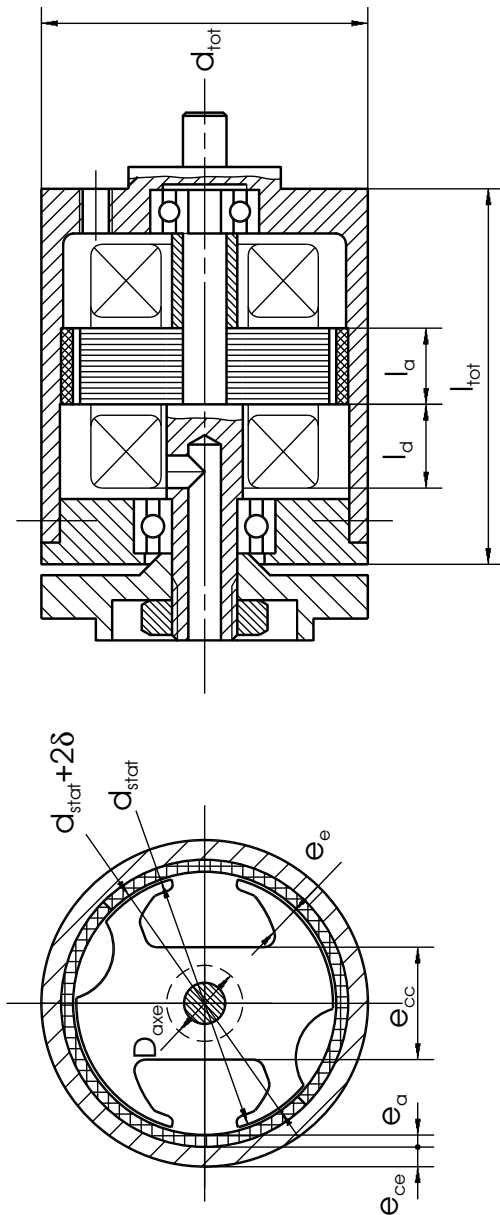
Vue d'ensemble du moteur / définition des symboles
